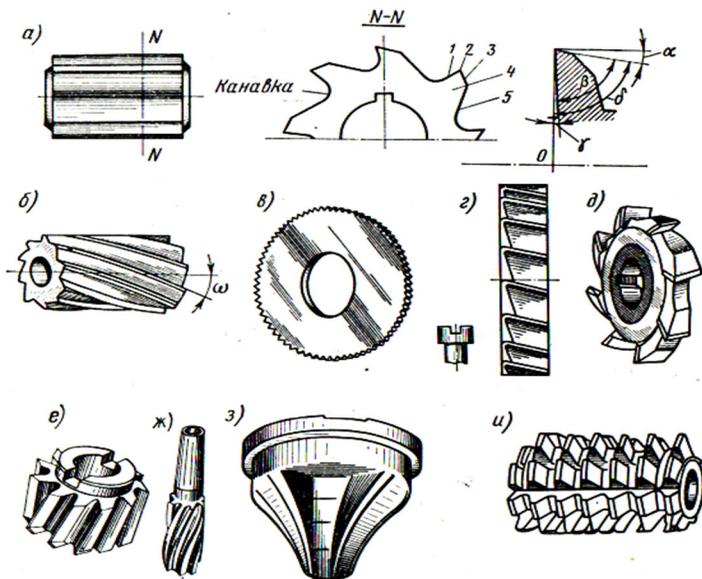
Основные типы фрез: а – цилиндрическая прямозубая; б – цилиндрическая с винтовыми зубьями; в – дисковая пазовая; г – дисковая двусторонняя; д – дисковая трехсторонняя; е – торцовая; ж – концевая; з – пальцевая модульная; и – червячная
